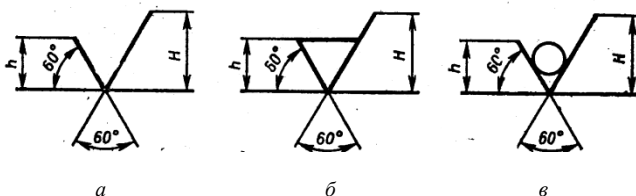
Знаки шероховатости:  $h$  — высота размерных чисел;
